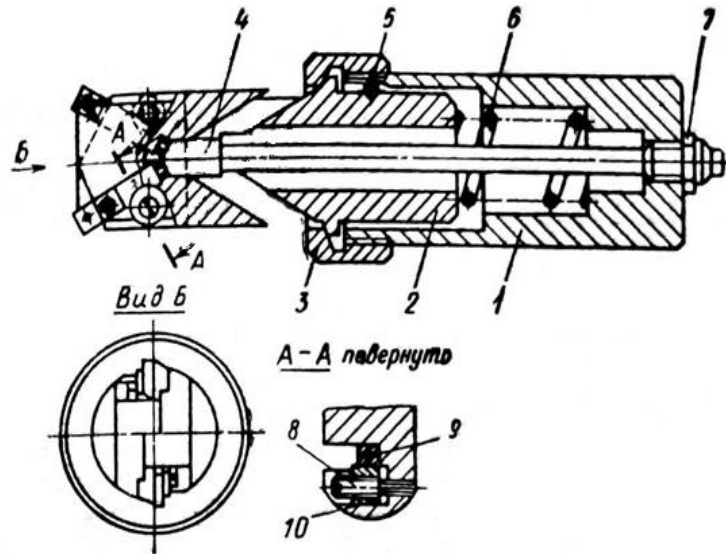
Приклад гойдальної дволезової розвертки для верстата-автомата
